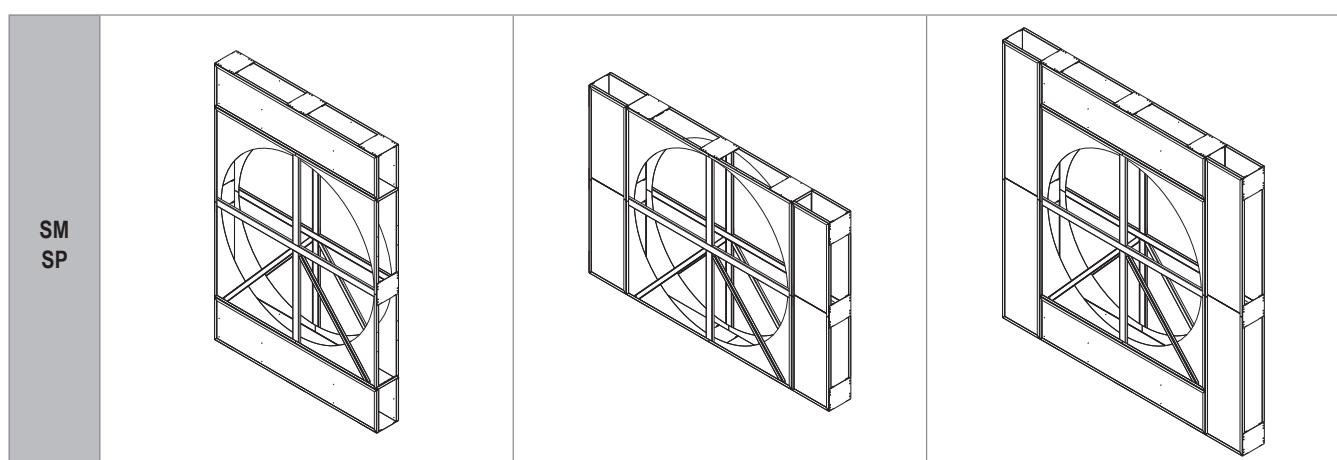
Anpassung der Gehäusegrösse mit Boxen
